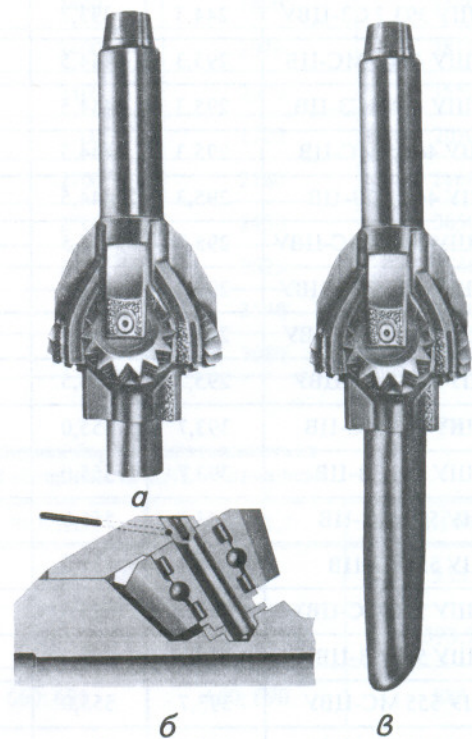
Розширювачі виробництва компанії «Grant Oil Tool Company» (США): а—шарошковий; б—переріз вузла кріплення шарошки в розширювачах; в—шарошковий для буріння ПСС із моноблочним корпусом;
